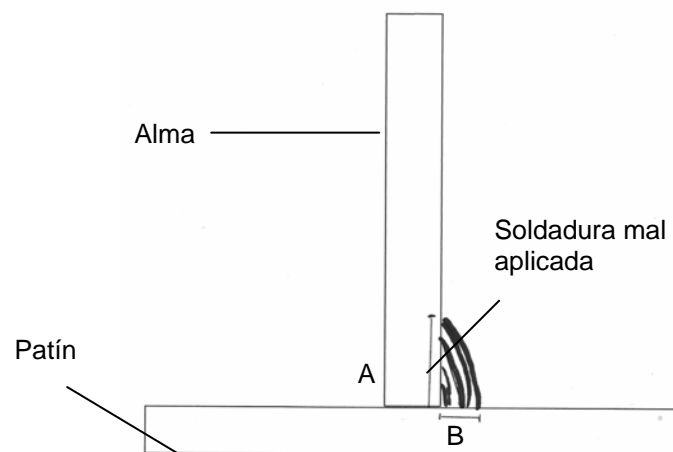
Soldadura mal aplicada, abarca más a el alma que al patín $A > B$
